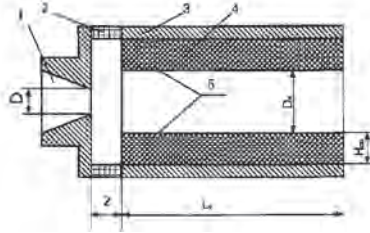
Расчетная глушителя шума эжекторного типа, состоящего из сопла 1, прикрепленного к корпусу 3 глушителя с зазором «Z» через акустически прозрачное кольцо 2, звукопоглощающей вставки 4 с акустически прозрачной пленкой 5.
